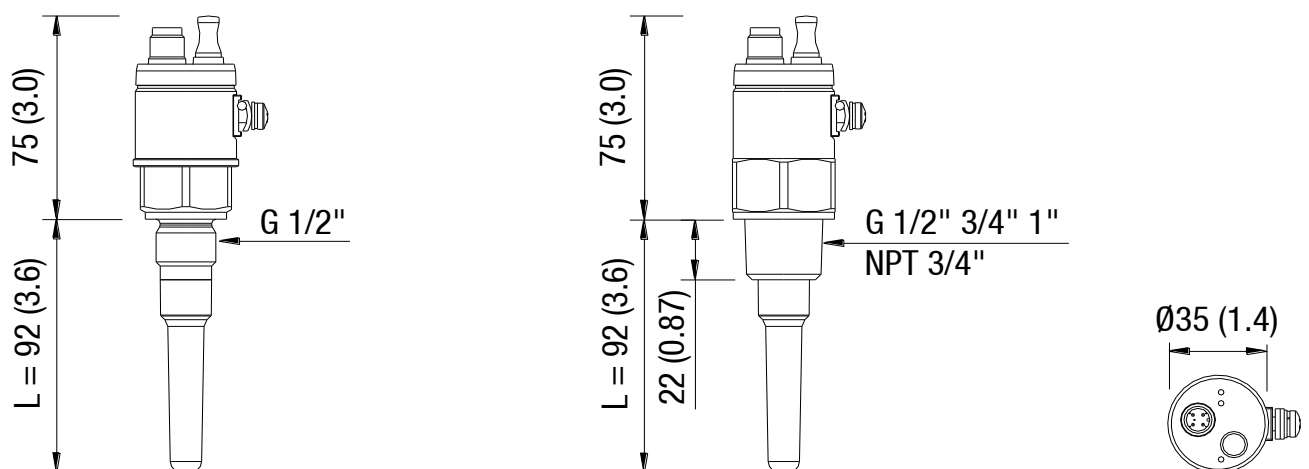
Abmessungen CN 7120, Gehäuse Ø 35 mm
